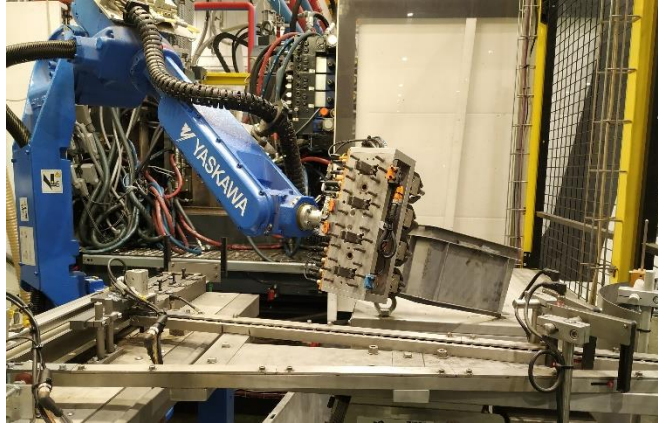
Sistema de fabricación flexible ubicado en el laboratorio A5.4.
